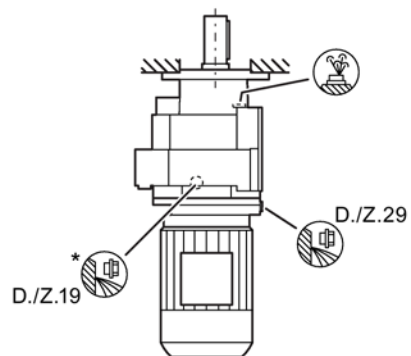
Монтажные положения для цилиндрического редуктора DB/ZB в исполнении на лапах / с фланцем, типоразмеры 39–89
